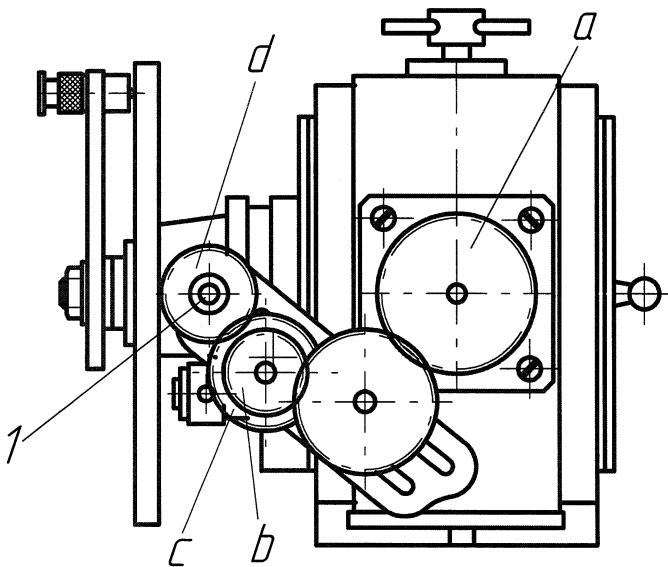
Схема установки сменных зубчатых колес в гитару дифференциального деления
